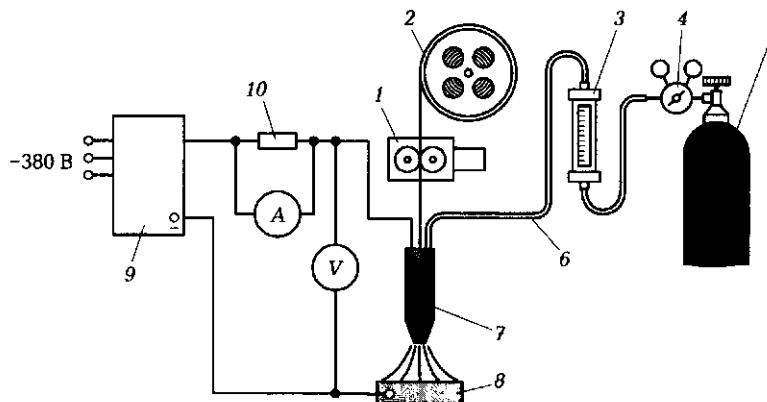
Схема сварочного поста для выполнения сварки полуавтоматом углекислым газом:
